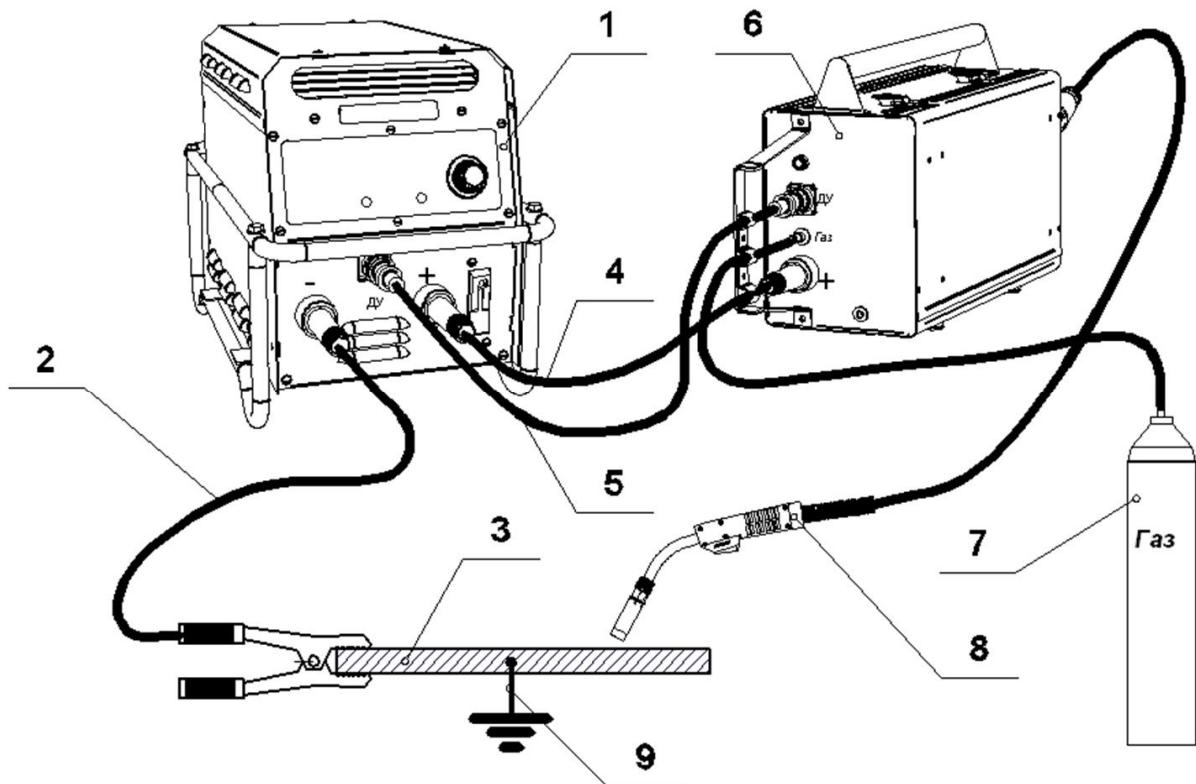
Пост полуавтоматической сварки.
